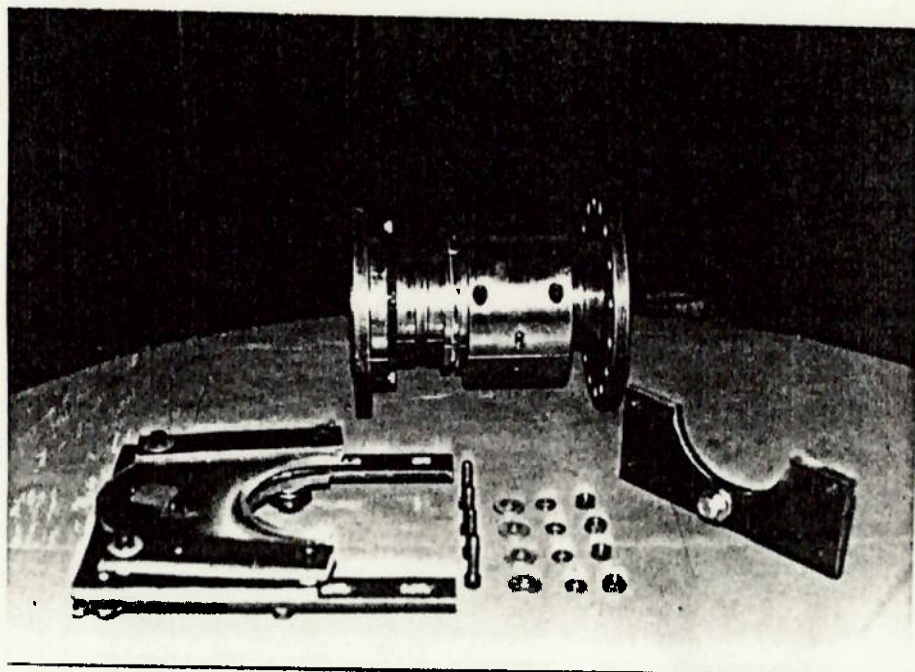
Eixo com carcaça montada, captador óptico instalado no suporte: vemos o eixo de torção com a carcaça montada fixa à flange esquerda com parafusos; à frente vemos o captador óptico elíptico em acrílico instalado na parte inferior do suporte do captador.
